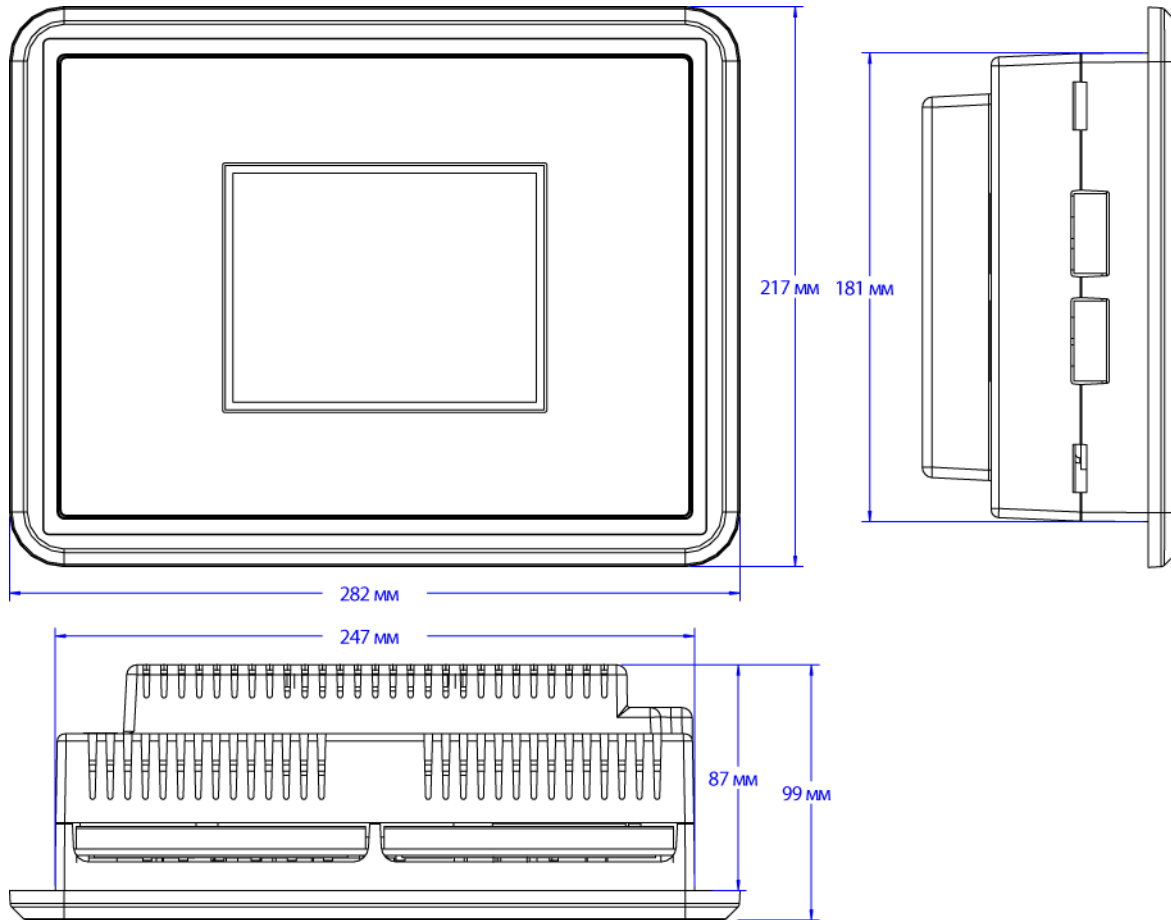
Пластмассовый корпус easYgen-3000 - размеры
